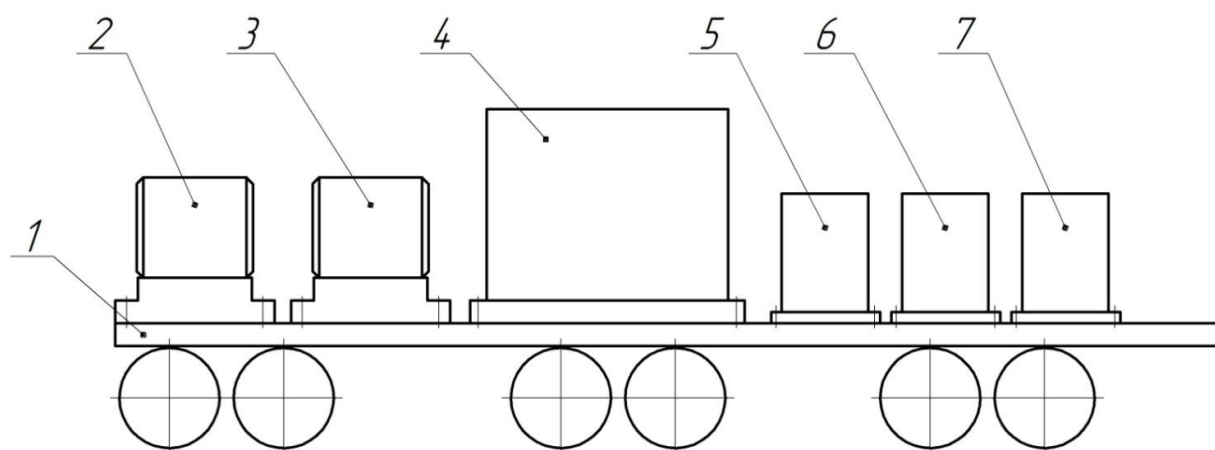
Передвижная установка для сварки в полевых условиях
